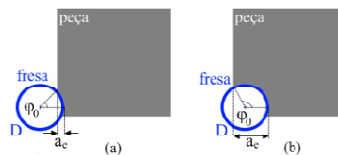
Ângulo de contato do inserto com o corpo de prova em (a) pequena profundidade radial de usinagem e (b) grande profundidade radial de usinagem
